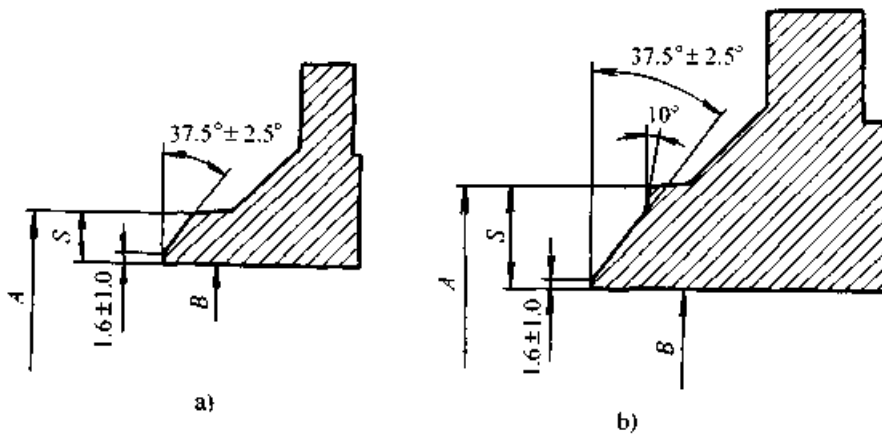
带颈对焊法兰与钢管连接的焊端坡口结构和尺寸
